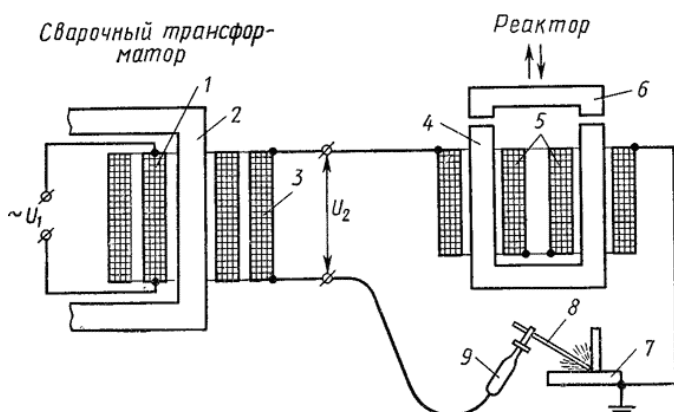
Принципиальная схема устройства и работы сварочного трансформатора
